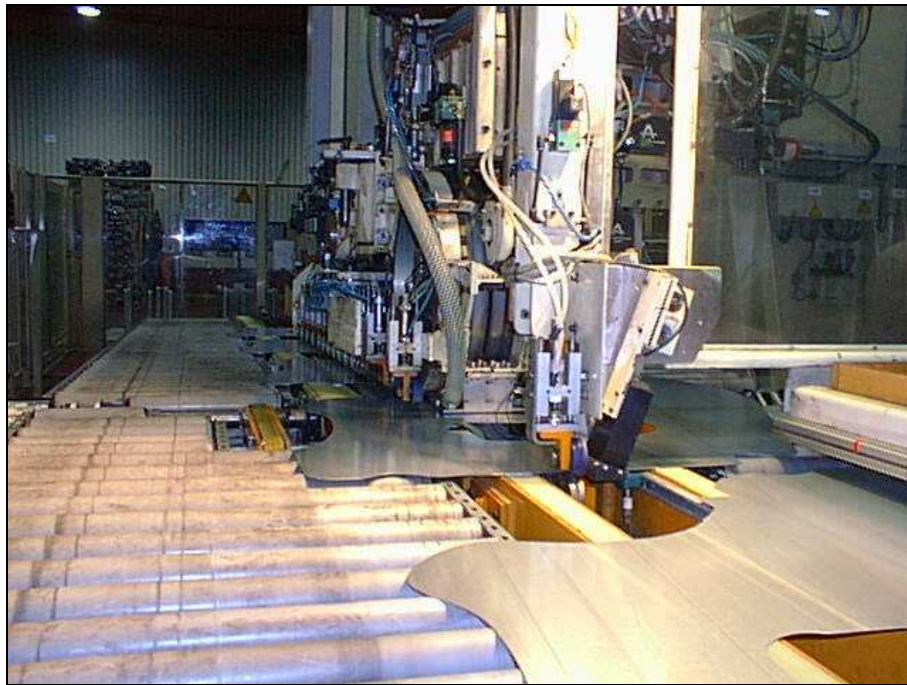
Inspector Sensor zur Nahtinspektion an Thyssen Nothelfer Conti - Laserschweißanlagen (mit freundlicher Genehmigung der Thyssen Fügechnik GmbH und der Thyssen Nothelfer GmbH)
